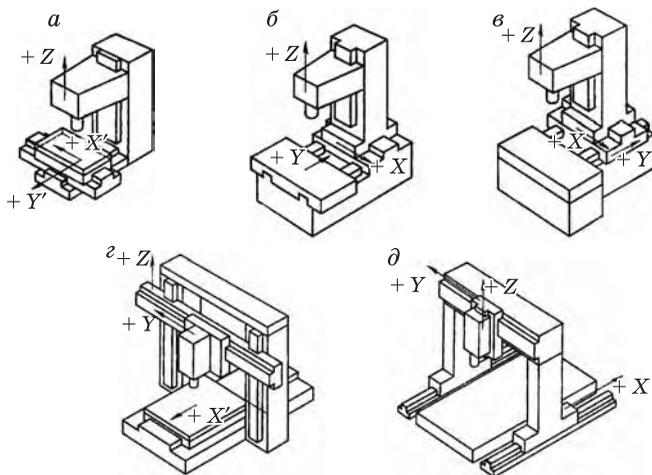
Примеры компоновок многоцелевых станков сверлильно-фрезерно-расточной группы с вертикальным расположением шпинделя:
